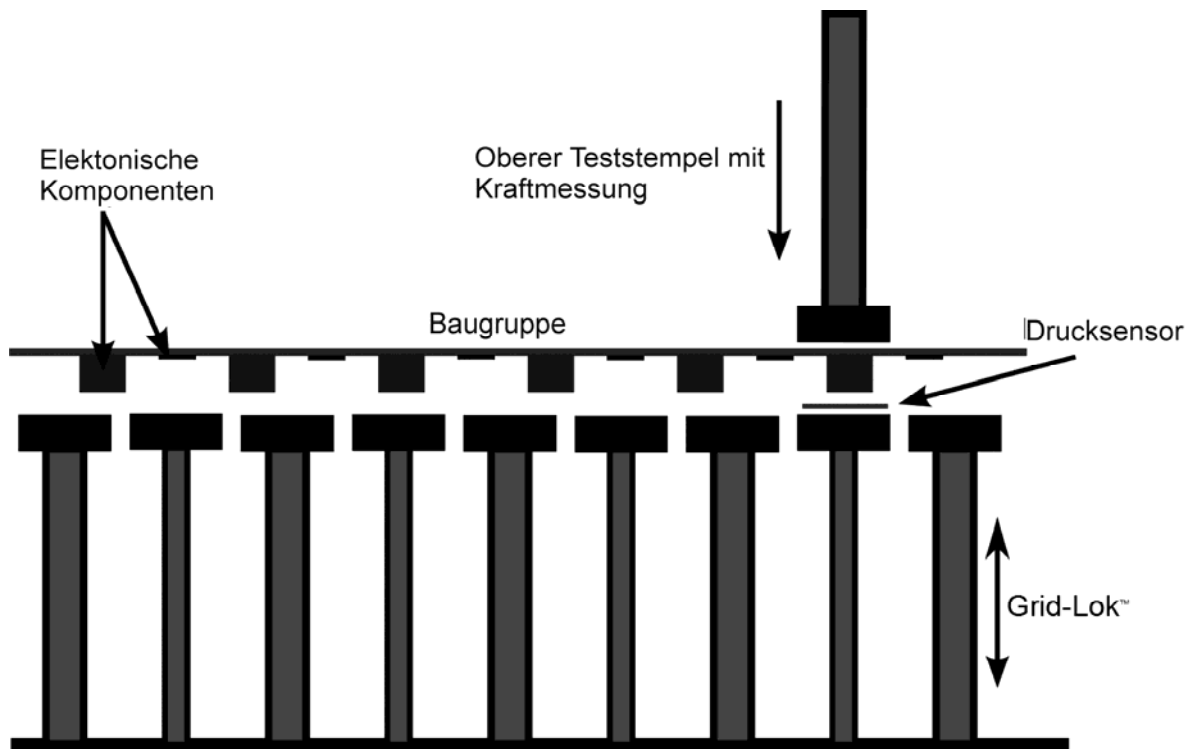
Schematischer Versuchsaufbau für den Test zur mechanischen Baugruppenbelastung.
